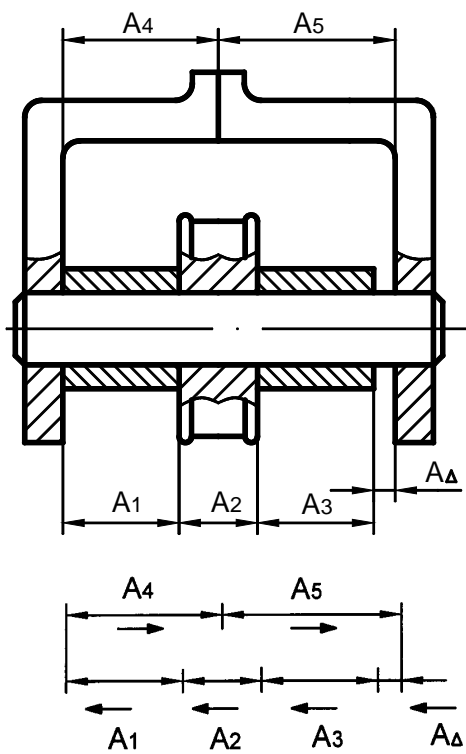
Эскиз узла и схемы сборочной размерной цепи
